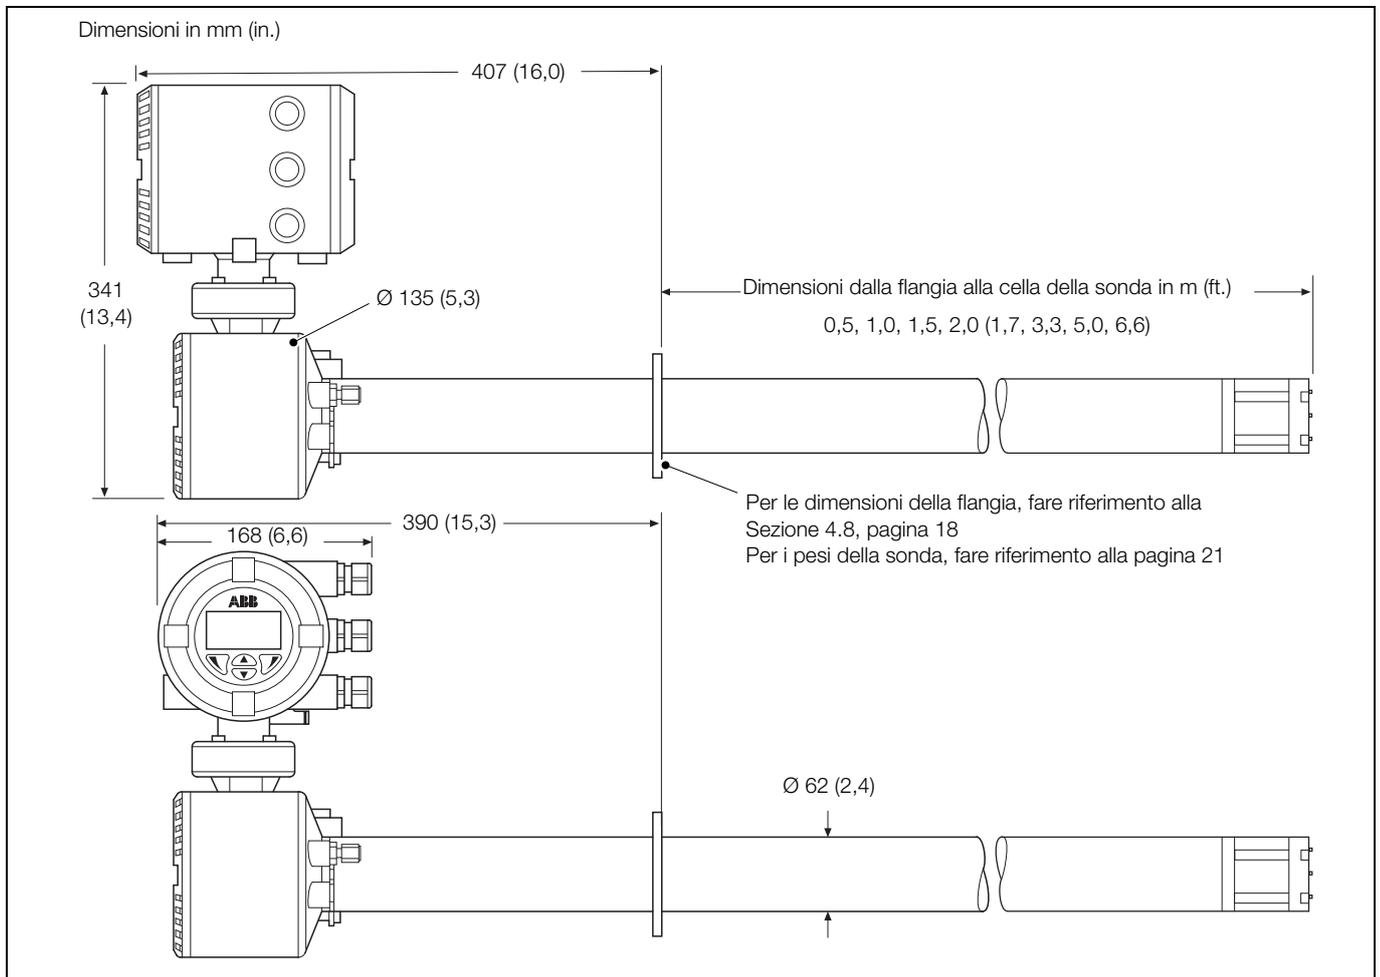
Dimensioni complessive – sonda Endura AZ30 integrata
